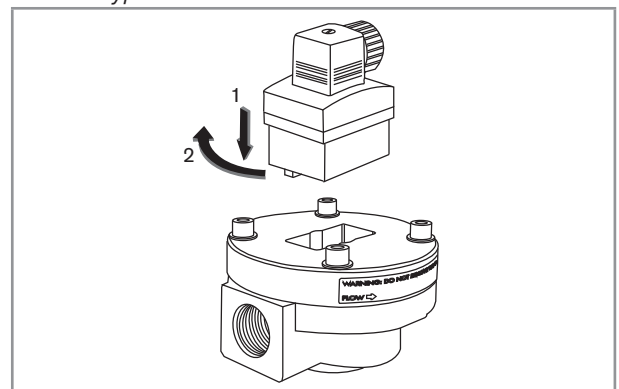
Montage des SE30 Ex auf ein Sensor-Fitting Typ S070 oder Typ S077
